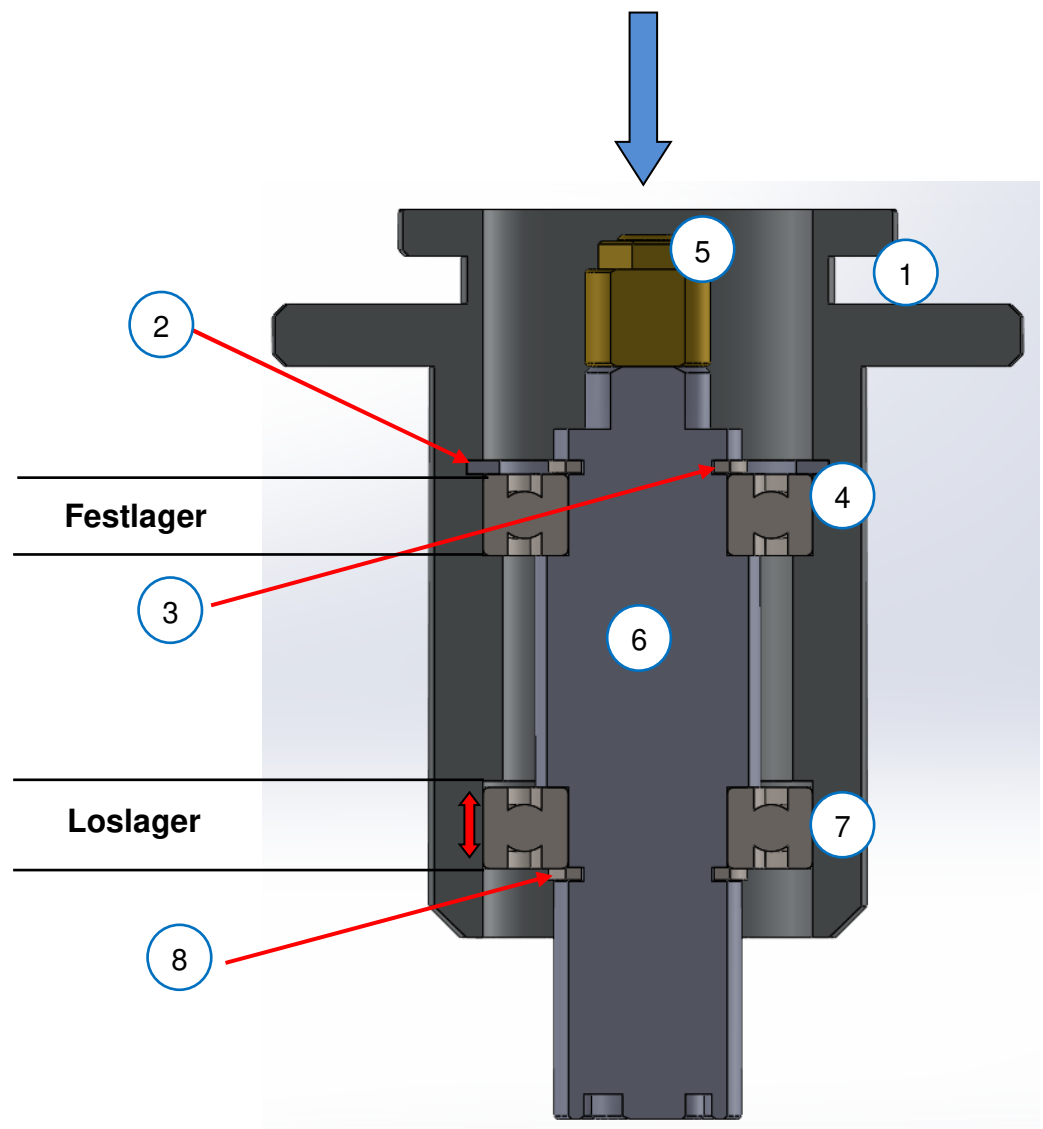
Werkzeughalter 1 Schnittansicht 1
